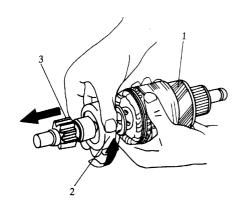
小齿轮组件与电枢的组装 1. 电枢 2. 小齿轮组件 外座圈 3. 小齿轮
